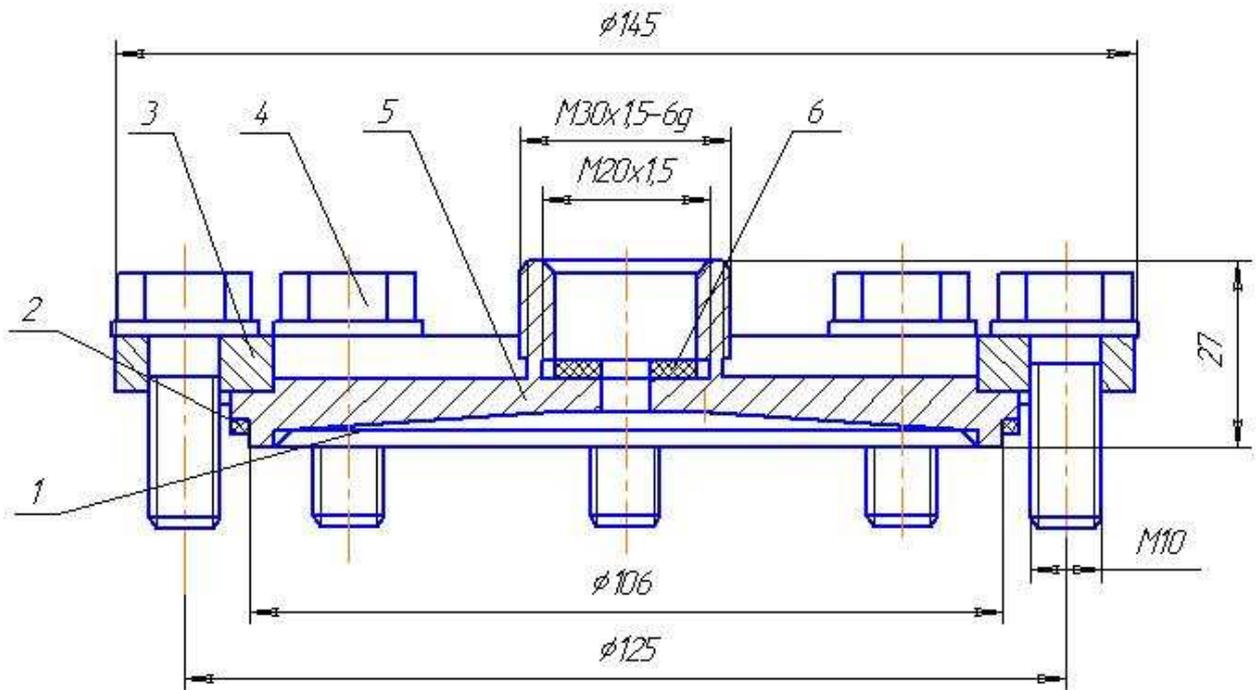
Конструкция, габаритные и присоединительные размеры
